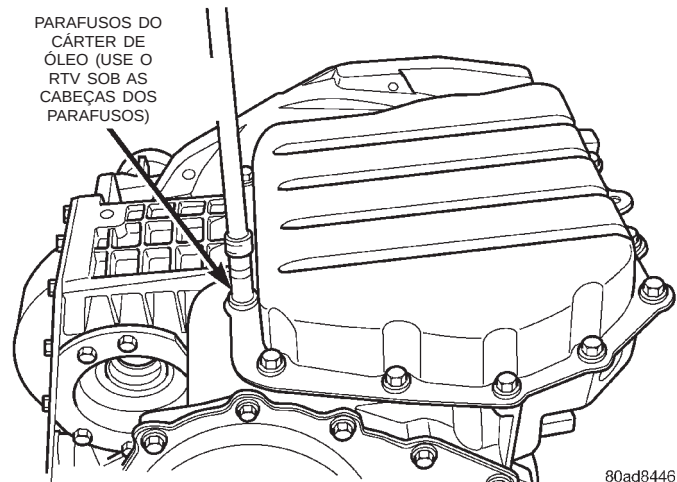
Remoção dos Parafusos do Carter de Óleo
